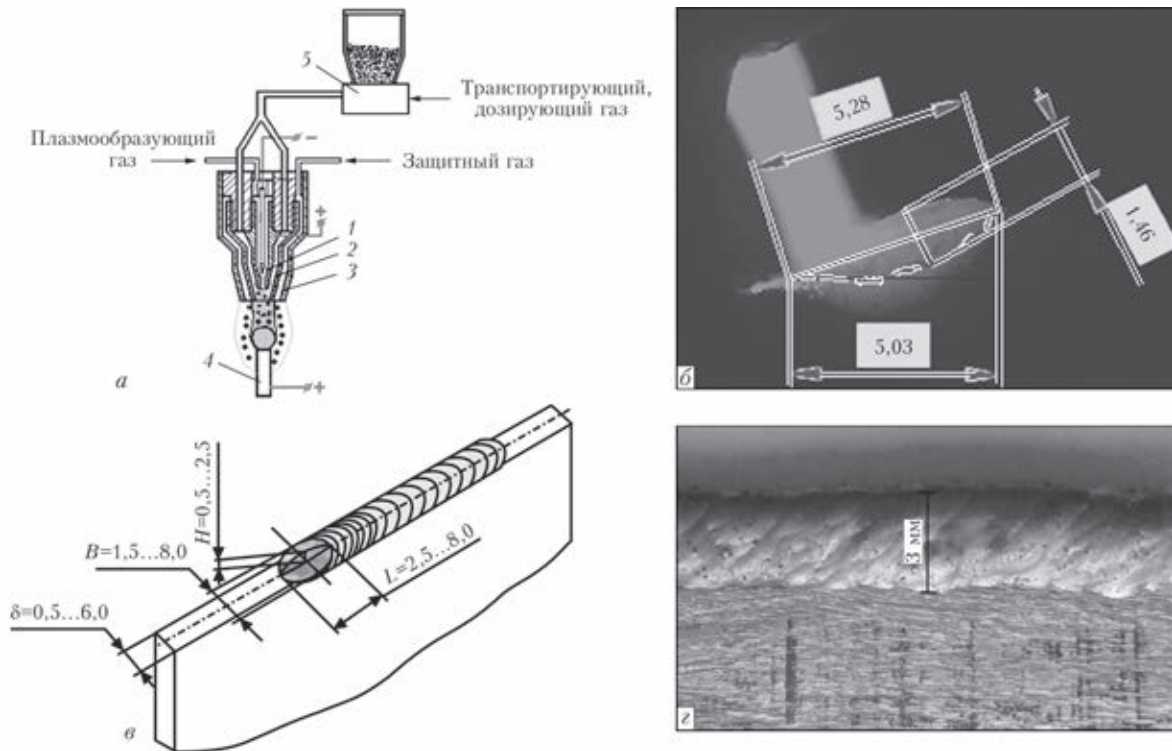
Схема процесса микроплазменной порошковой наплавки (а), внешний вид сварочной ванны (б), типичные ее размеры (в), внешний вид наплавленного валика (г) (а: 1 — плазменное сопло; 2 — фокусное сопло; 3 — защитное сопло; 4 — изделие; 5 — питатель для подачи порошка)
